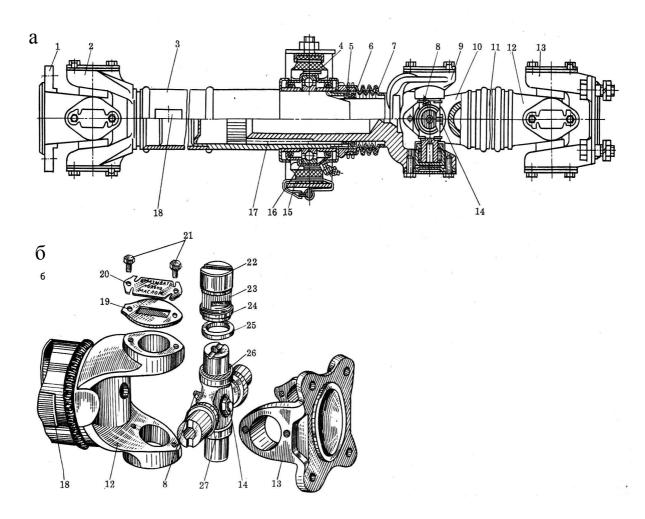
Карданная передача и детали карданного шарнира: a — карданная передача;  $\delta$  — шарнир неравных угловых скоростей; 1, 2, 9, 10, 12 и 13- вилки; 3 - промежуточный вал; 4 - резиновая подушка; 5 - резиновый сальник;  $\delta$  — войлочный сальник; 7 - защитный чехол; 8 — центральная масленка; 11 - основной карданный вал; 14 — предохранительный клапан; 15 - кронштейн опоры; 16 - шарикоподшипник; 17 - шлицевое соединение; 18 - балансировочная пластина; 19 — крышка; 20 - стопорная пластина; 21 — болт; 22 — стакан; 23 - игольчатый подшипник; 24 - стопорная шайба; 25 - сальник; 26 — корпус сальника
